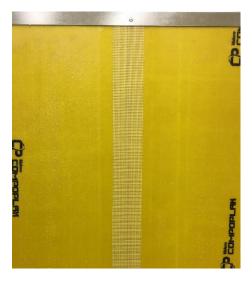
Unión de los paneles mediante soldadura química (malla de fibra de vidrio + resina de poliéster).
